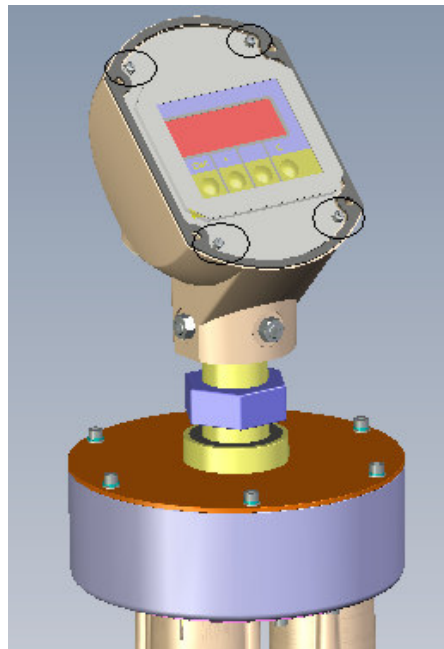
Befestigungsschrauben der Sensorelektronik
